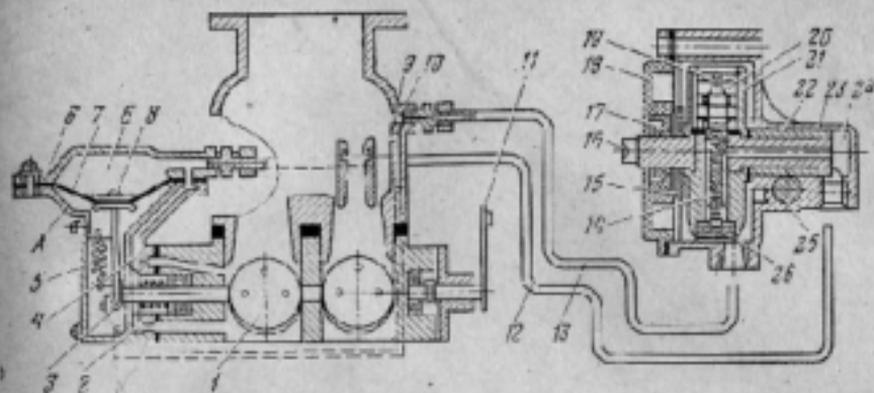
Схема пневмоцентробежного датчика ограничителя частоты вращения коленчатого вала двигателя:
